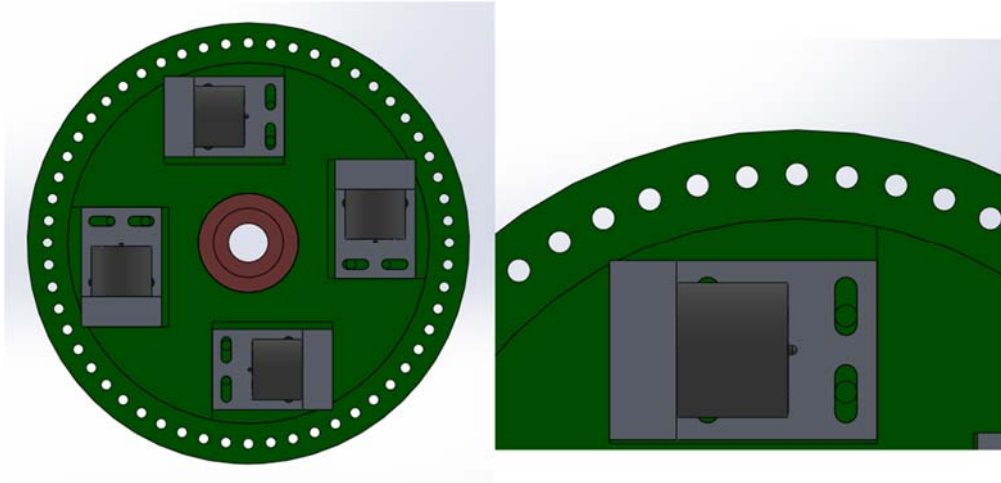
Ranurados para posicionamiento de los soportes (vista general a la izquierda, vista en detalle a la derecha)
